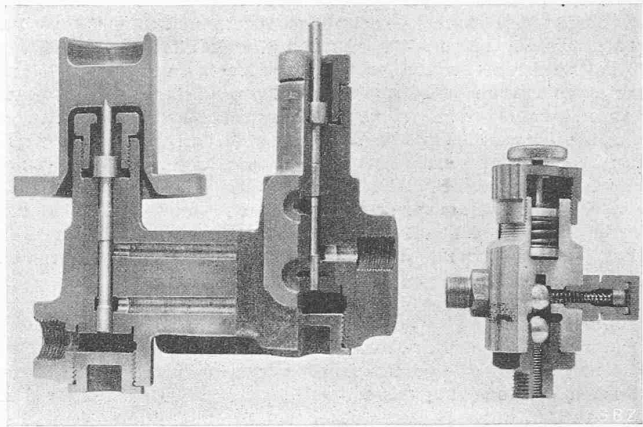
Pneumatische Differentialdruck-Steuervorrichtung. Links frühere Ausführung mit zwei gewichtsbelasteten Kolben, rechts heutige Ausführung mit Doppelkugel. Gewichtsverminderung auf  $\frac{1}{4}$
